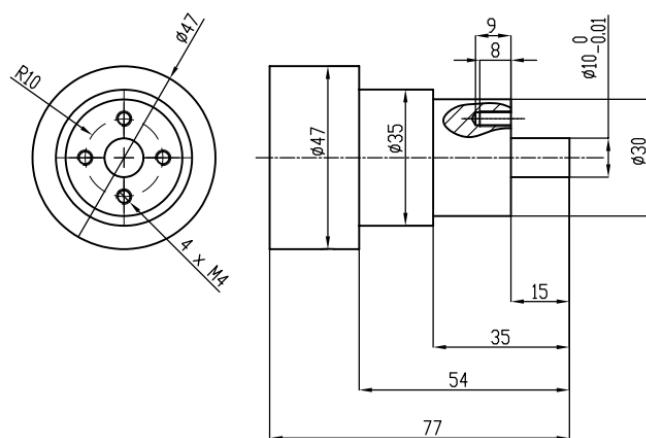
Gambar Teknik Rumah *Lower Bearing
